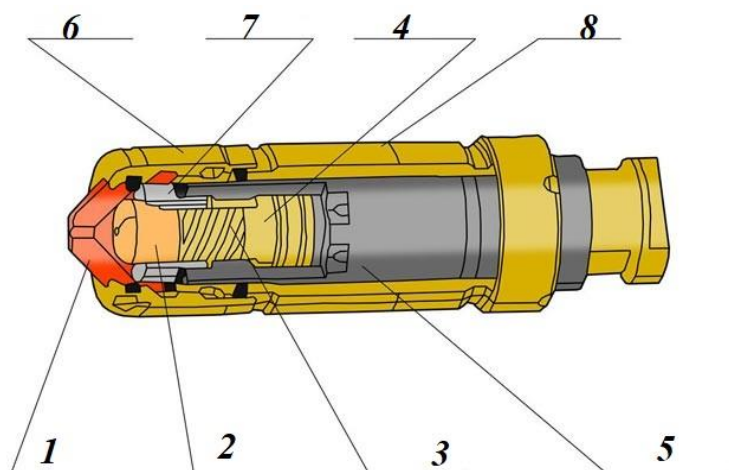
Конструкція плазмотрона. 1 – Сопло, 2 – Електрод, 3 – Механізм закрутки повітряного потоку, 4 – Електродний вузол, 5 – Корпус, 6 – Захисний ковпачок, 7 – Ізоляційна втулка, 8 – Захисний кожух.
